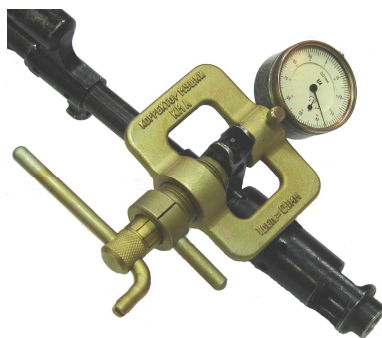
Установка КМА для смещения ползка мушки влево
